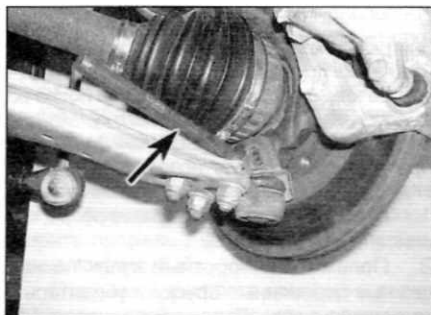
, а. С помощью маленького зубила (отмечено стрелкой) разожмите прорезь в поворотном кулаке...
